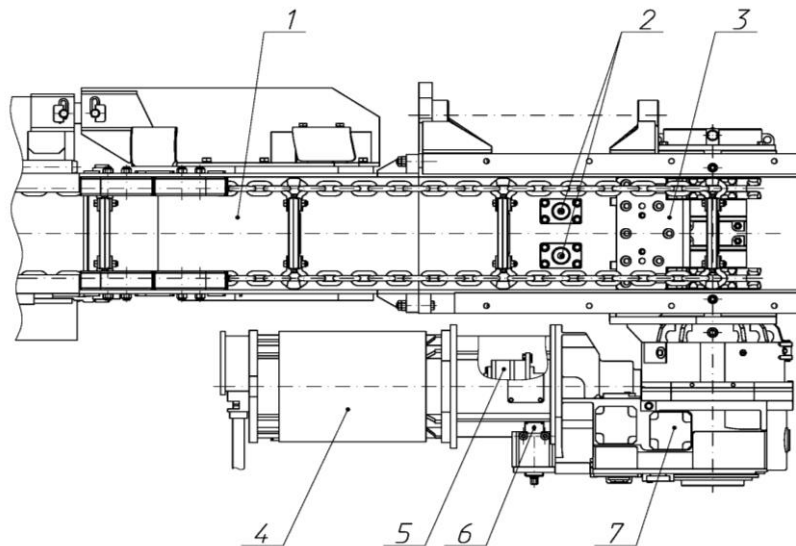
Приводной блок конвейера СПД 26 с продольным расположением двигателя:
